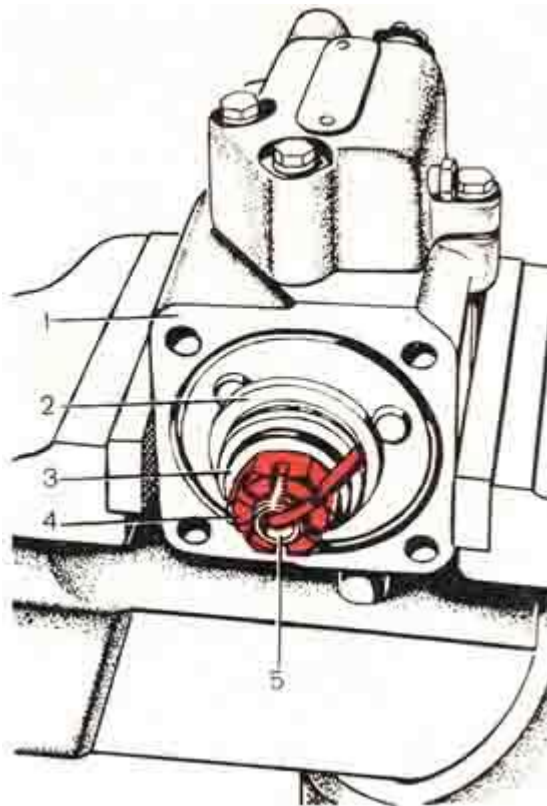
Розбирання розподільника та зняття черв'яка 1 – корпус; 2 – підшипник; 3 – шайба; 4 – сферична гайка; 5 – черв'як
